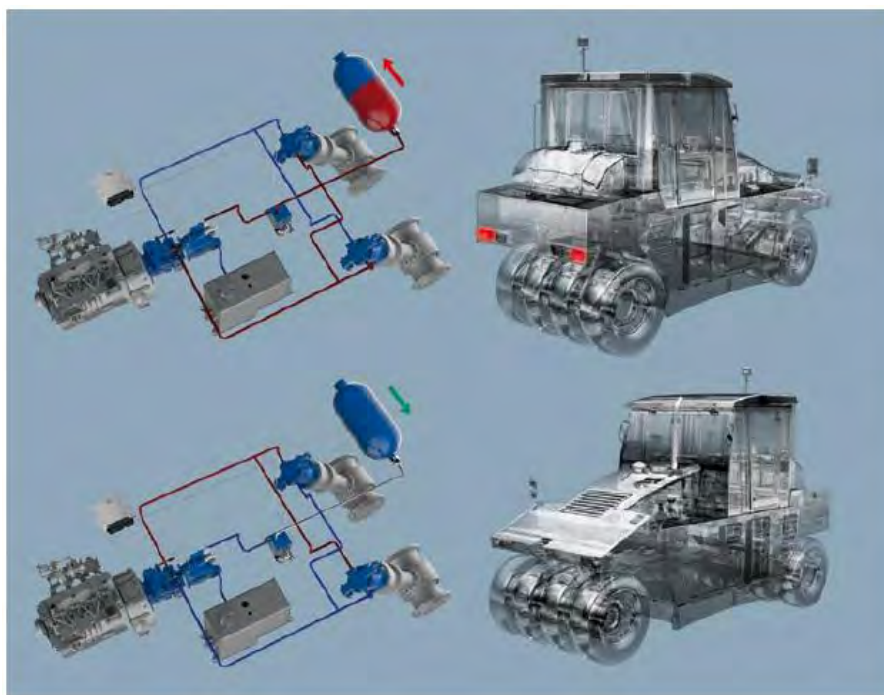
Pneumatikový válec s paralelním rekuperačním modulem Hydraulic flywheel [28]
